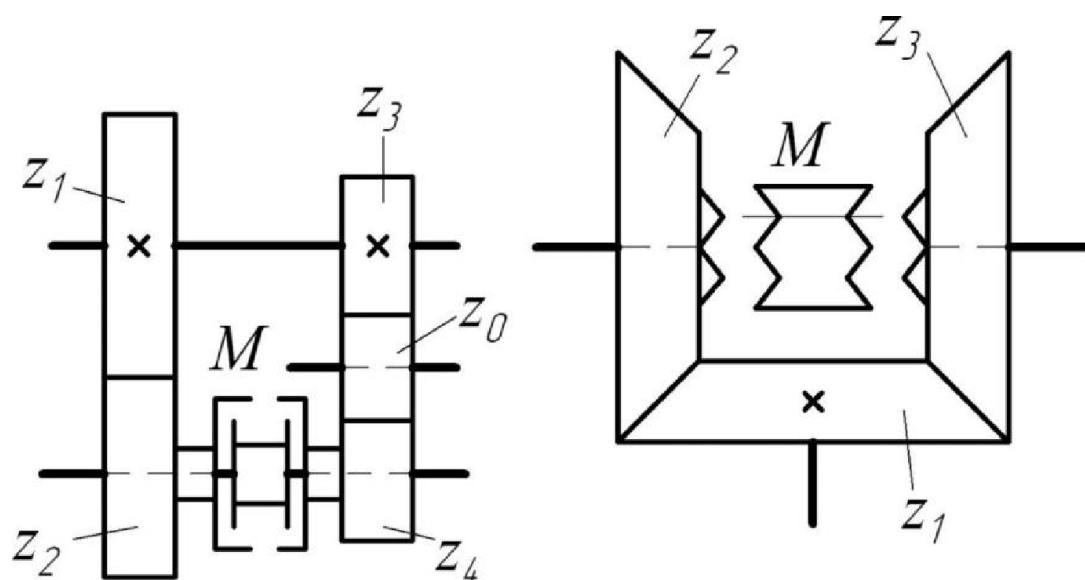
Реверсивні механізми металорізальних верстатів
